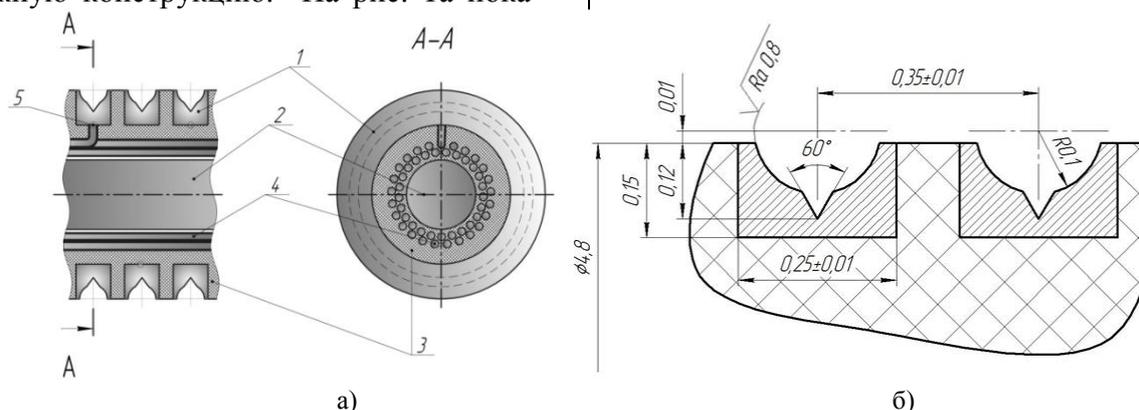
Схема конструкции коллекторов ГК-11, ГК-12 (а) и профиль поперечного сечения щеточной канавки (б): 1- контактное кольцо; 2- центральный валик; 3- компаунд (электроизоляция); 4- контактные провода; 5- пайка провода под кольцо
